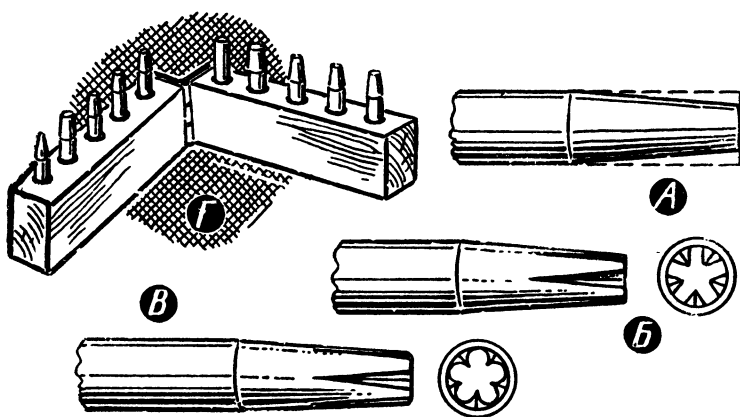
Изготовление чеканов: А — опиливание заготовки; Б — запылы; В — закругление края «цветка»; Г — подставка.
